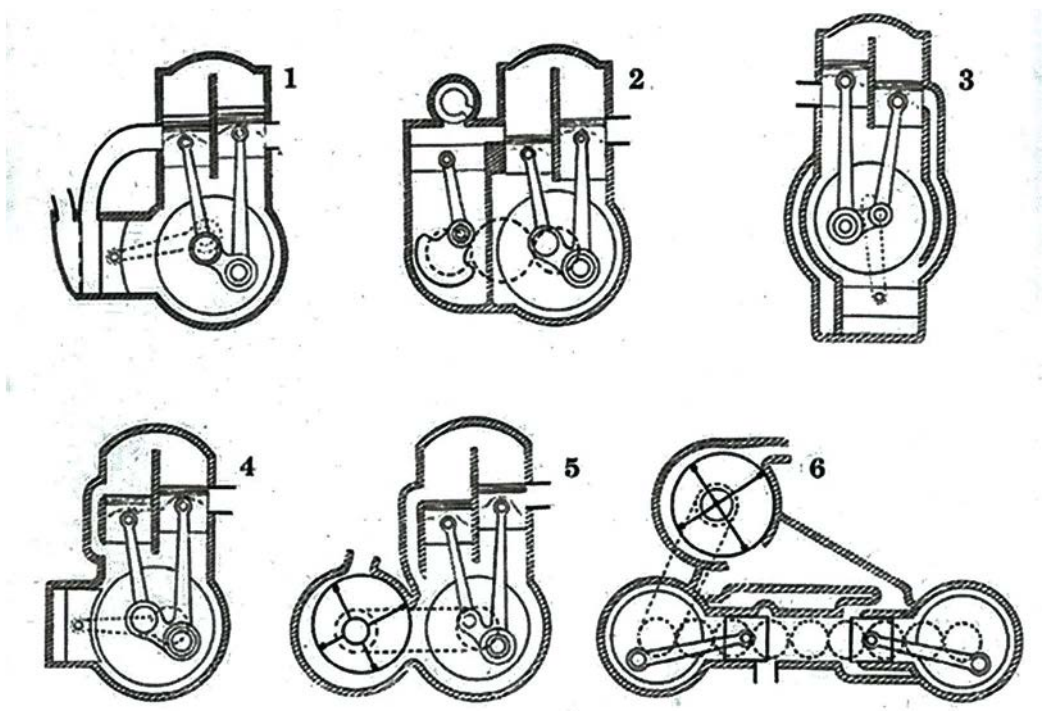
П-образные двигатели с грузовыми насосами разного расположения
